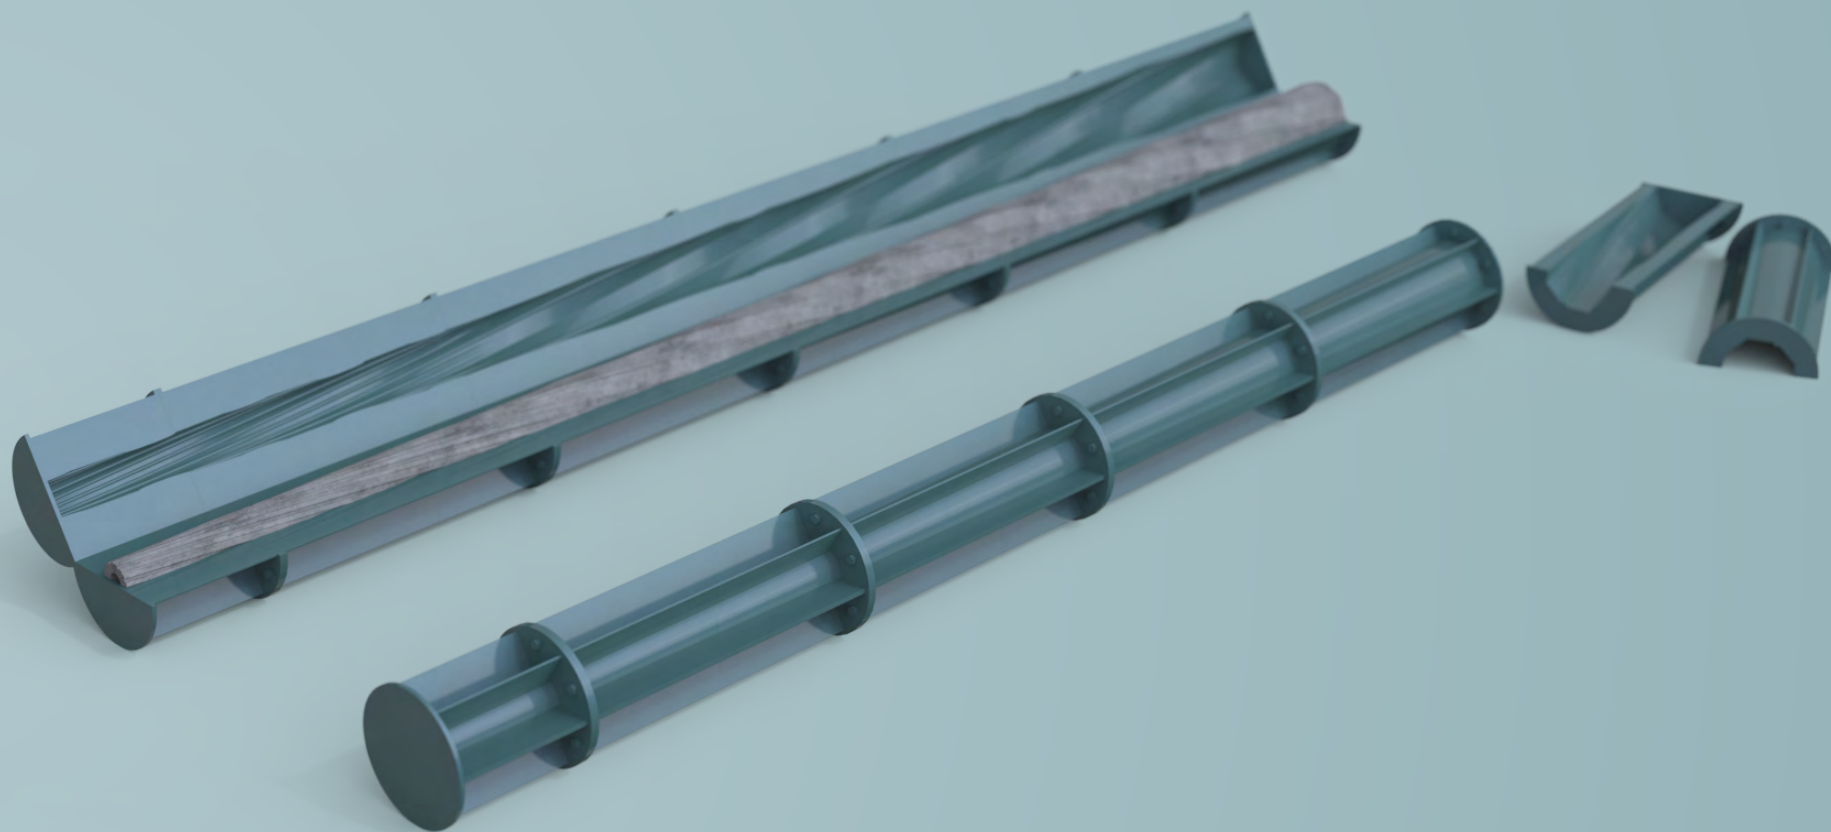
Propuesta de molde modular para ser usado en el proceso de manufactura, mediante la técnica de *Spun Cast* en un proceso de centrifugado.
